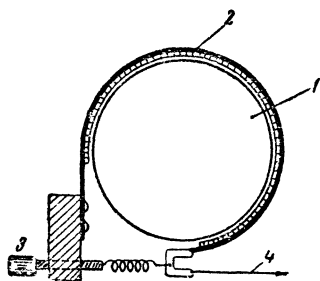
Устройство ленточного тормоза: 1 — тормозной шкив; 2 — тормозная лента; 3 — регулятор силы торможения; 4 — направление от-тормаживающей тяги
